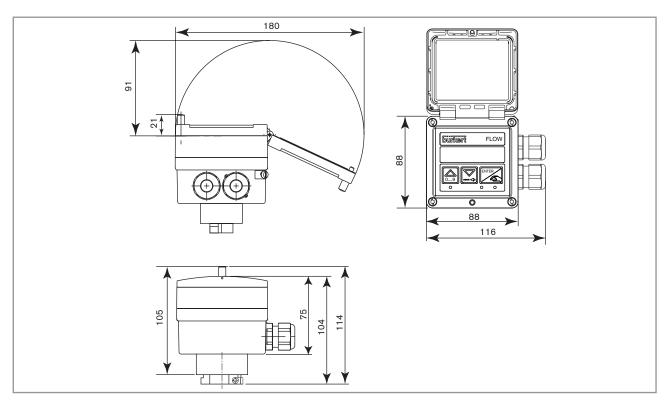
Dimensions du module électronique SE35 Batch [mm]
